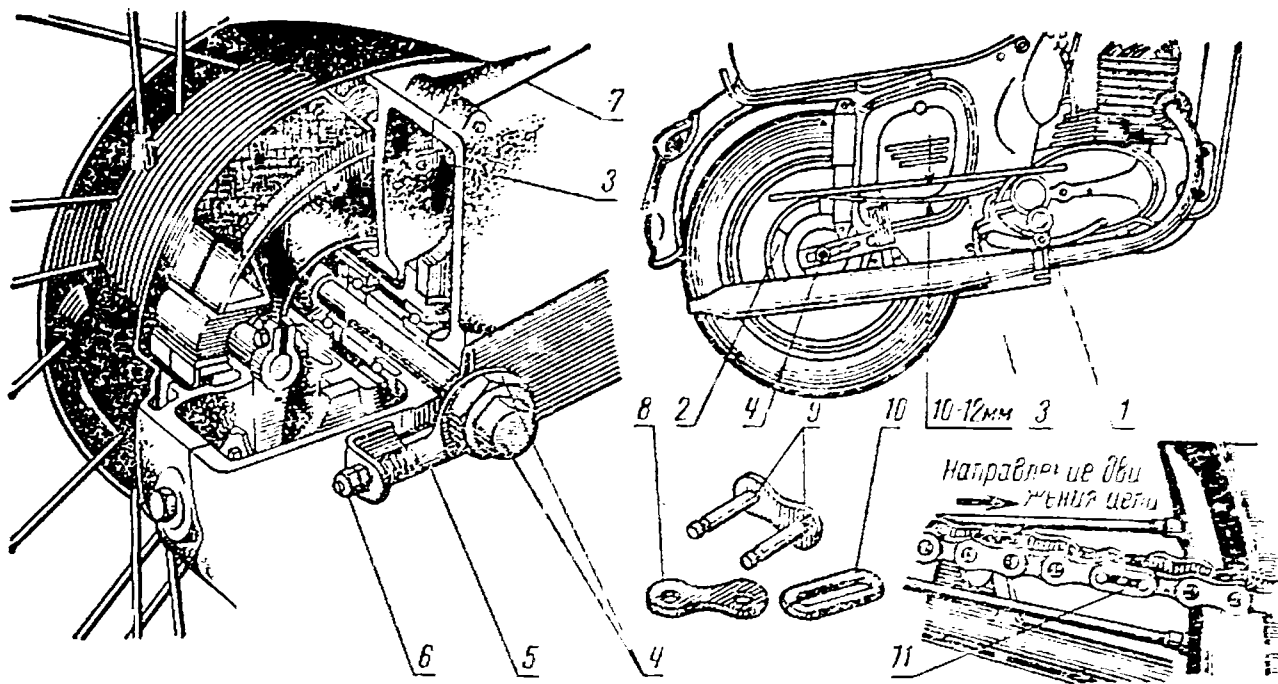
Задняя цепная передача с устройством для регулировки цепи:
